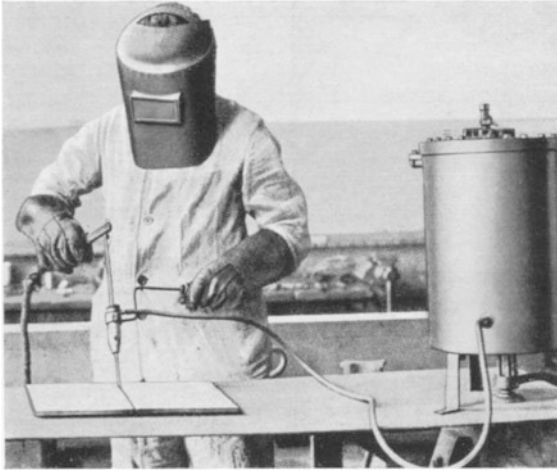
Das Schweißen mit dem Alexandergerät.
